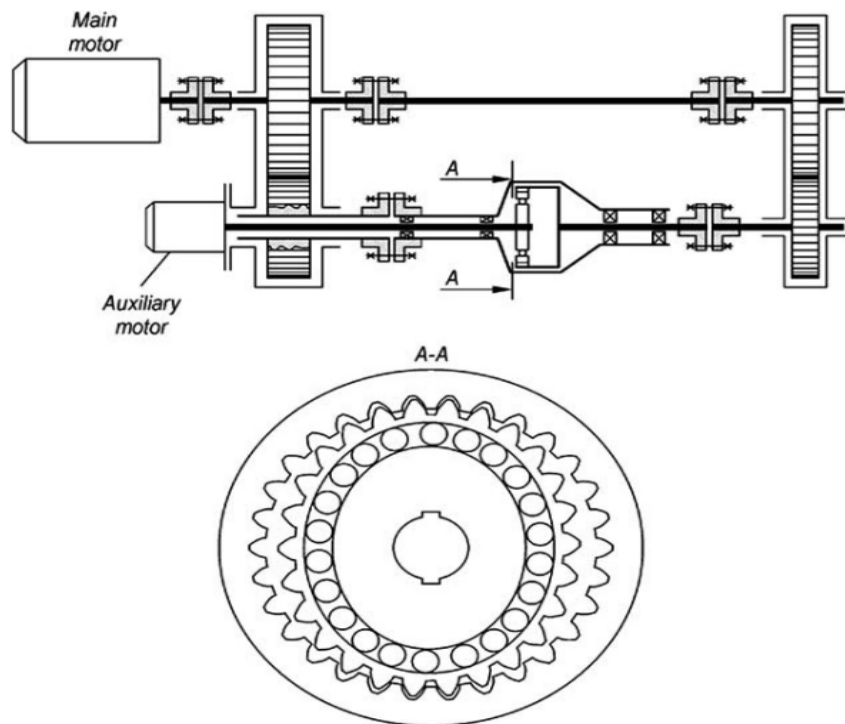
Banco Strain-Wave Gearing-Tubular Shaft⁽⁴⁾
